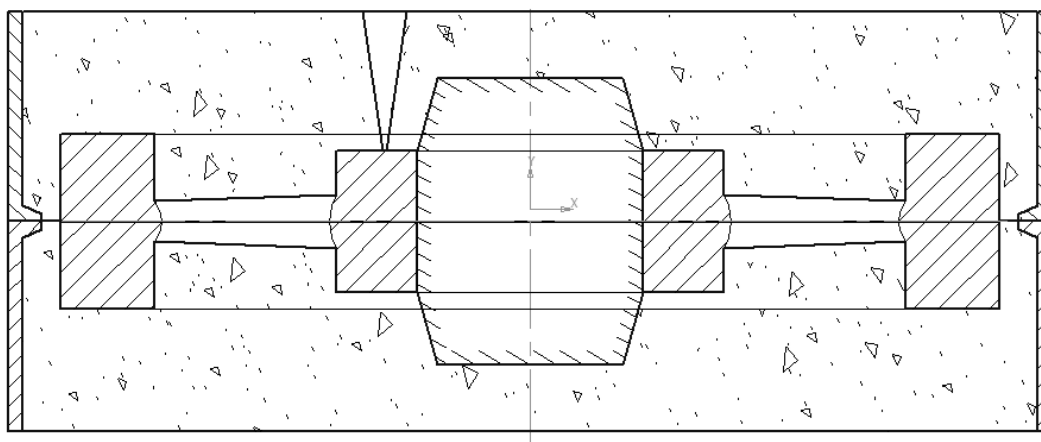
Отримання литої заготовки для деталі "Шківів"
